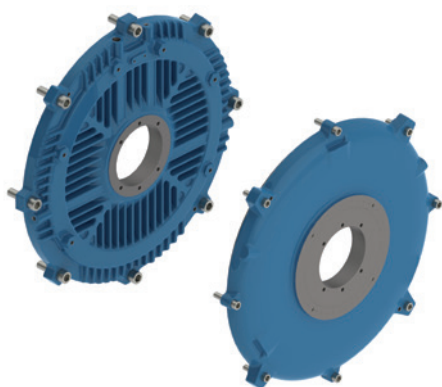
Tampa dianteira (esquerda) e tampa traseira (direita)
